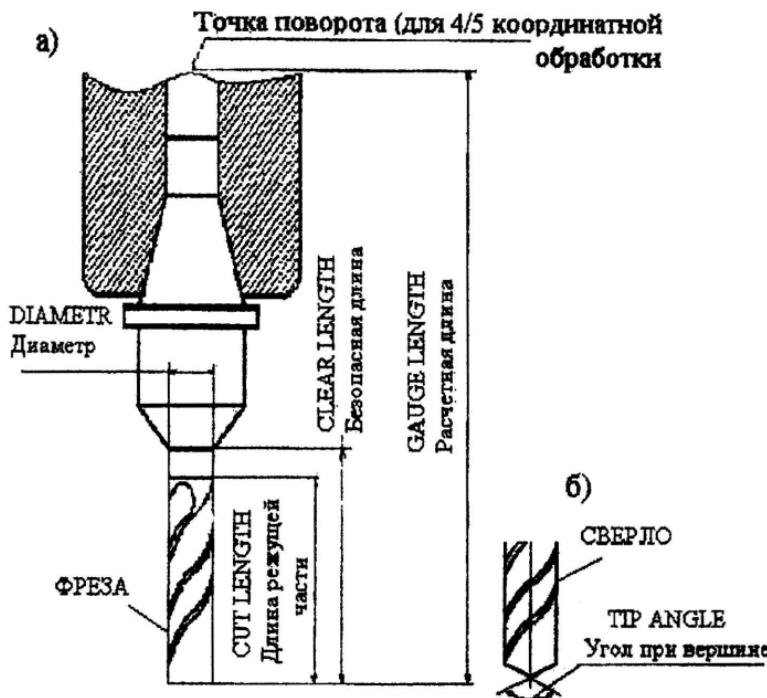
Геометрические параметры фрезерного инструмента:
